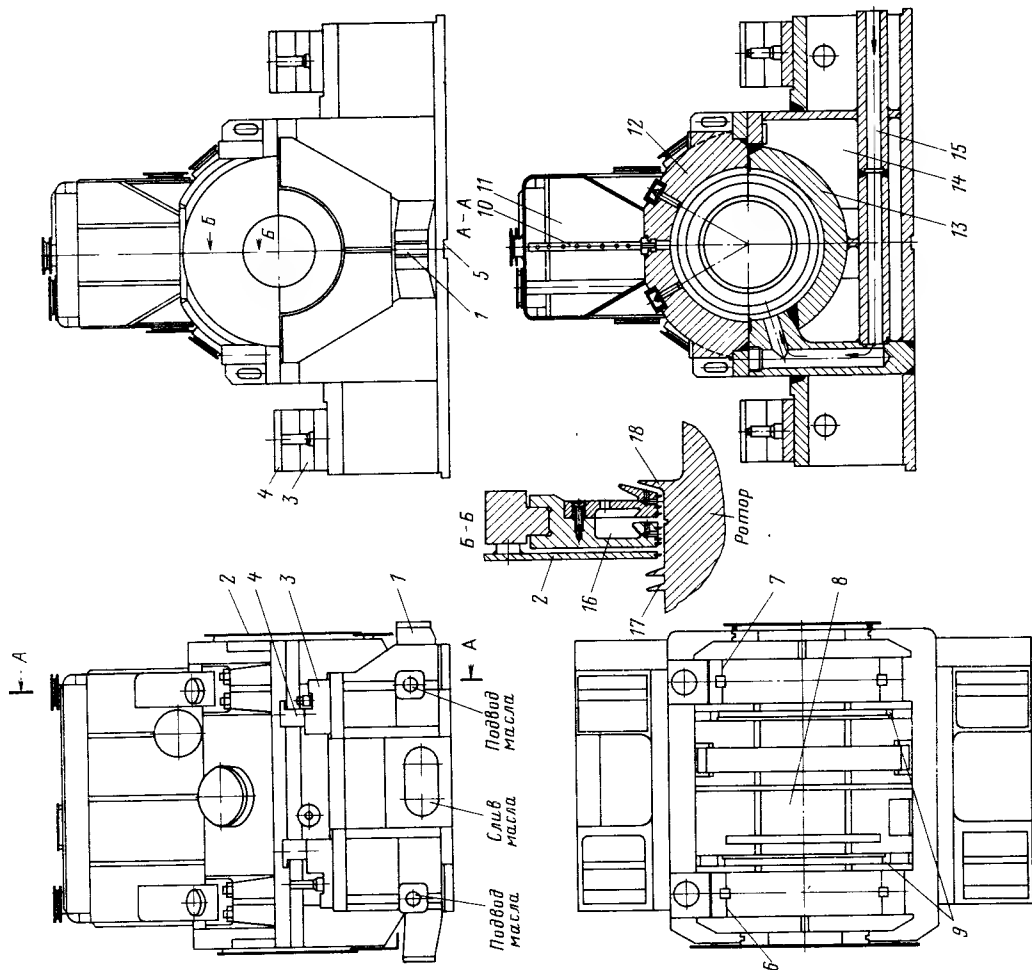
Корпус выносного подшипника турбины Т-250/300-240 ТМЗ
